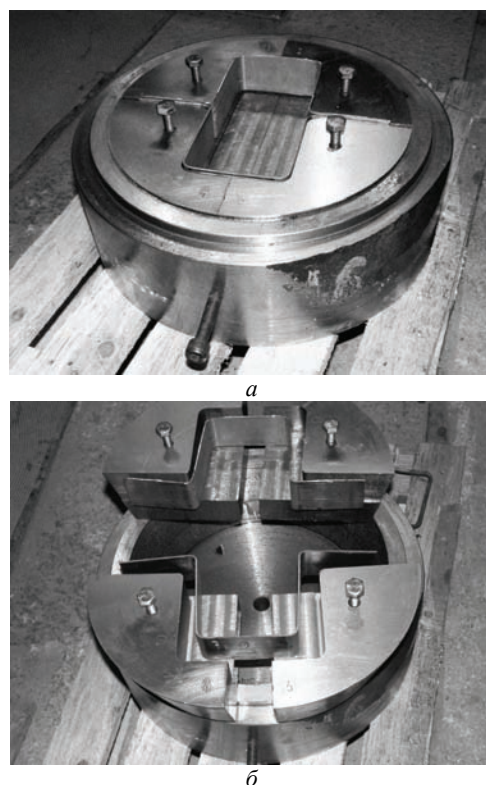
Штамп для ЭГ калибровки деталей:
